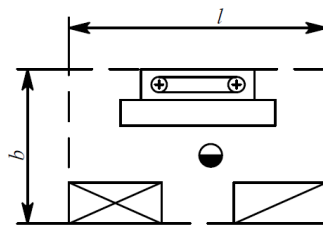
Рабочее место станка ШЛНСВ-2
